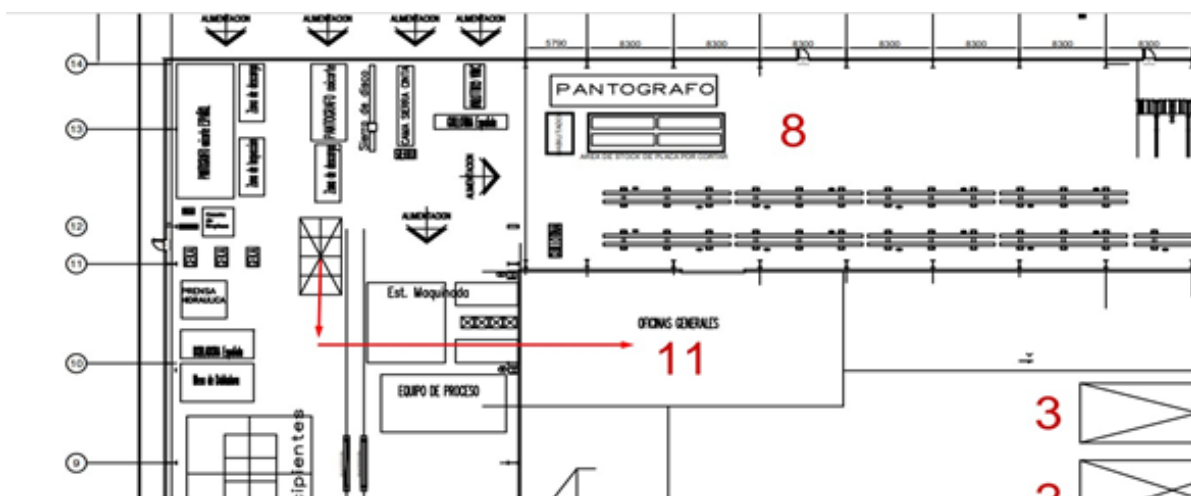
Layout prueba 4 de la Planta Durosa Santa Rosa SA, de CV.
